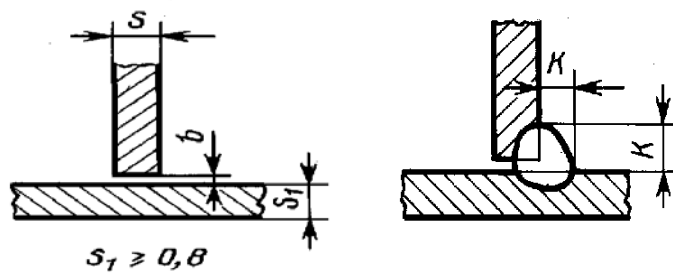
Эскиз сварного соединения Т1
